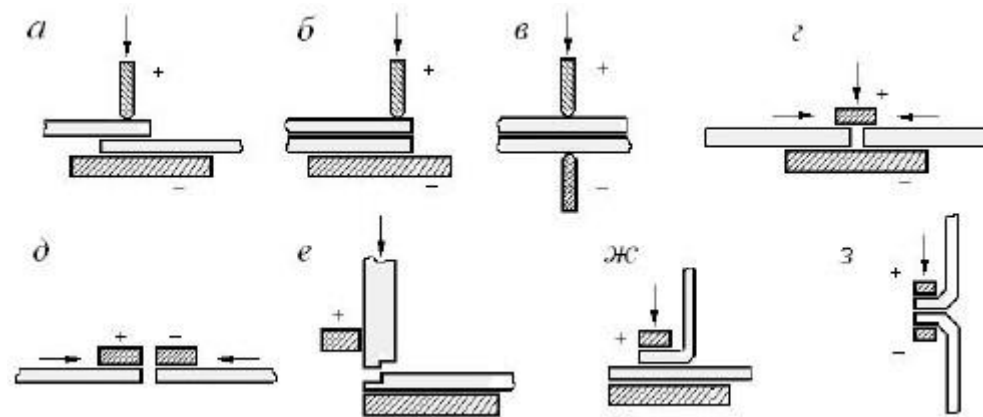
Виды сварных соединений и схемы размещения электродов при сварке: а, б, в – внахлестку; г, д, – встык; е – угловое; ж, з – с отбортовкой кромок; (+) - высоковольтный электрод; (-) – заземленный электрод
